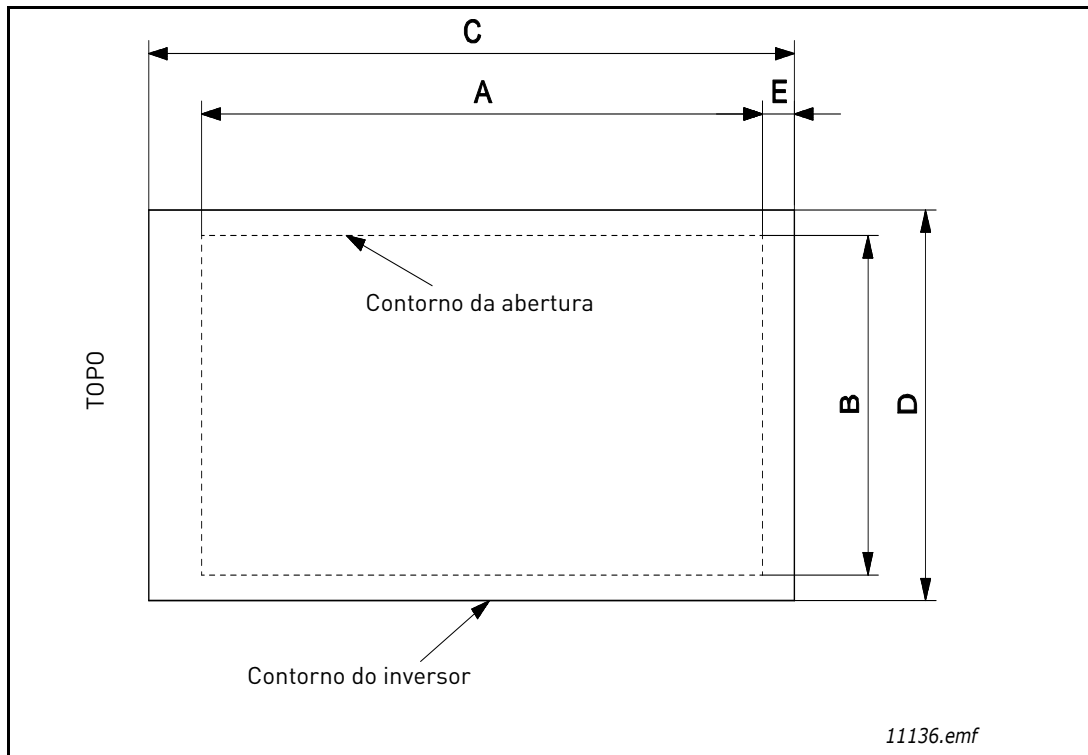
Dimensões do recorte para montagem com flange do MR4 ao MR9
